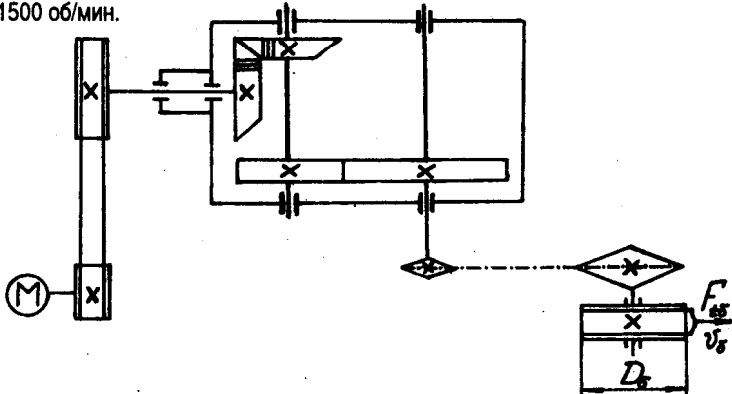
Кинематическая схема привода ленточного транспортера:
